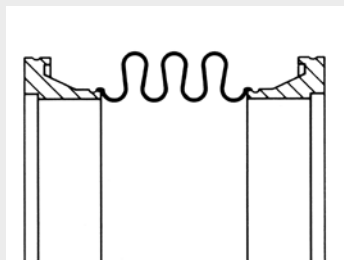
Axial-Kompensator mit Klammerflanschen
